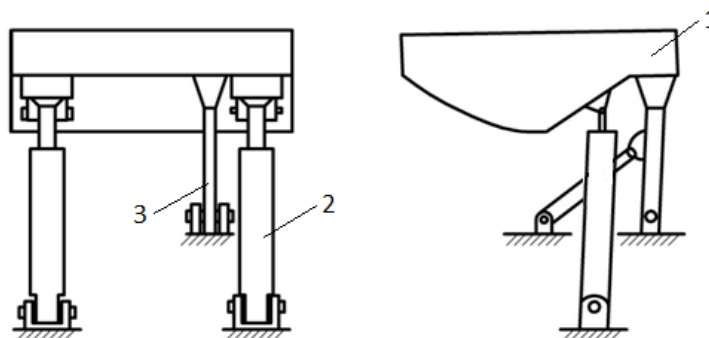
Механизм наклона печи: 1 – люлька; 2 – цилиндр наклона; 3 – цилиндр стопорный
